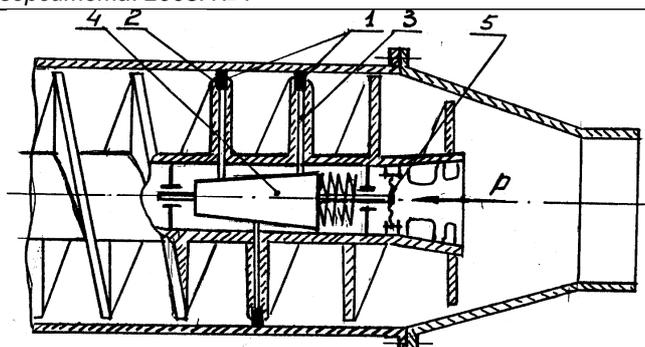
Конструкция шнеконапорного узла с уплотнительными кольцами: 1 – уплотнительное кольцо; 2 – паз гребня; 3 – толкатель; 4 – подвижный конус; 5 – мембрана
